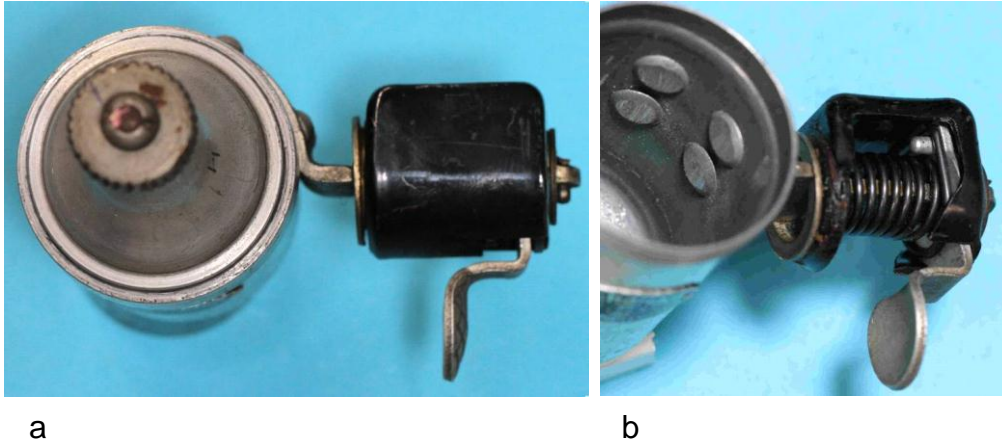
Kippvorrichtung am Gehäuse: a) Abgewinkeltes Pedal, b) Nietköpfe im Innenraum des Gehäuses
